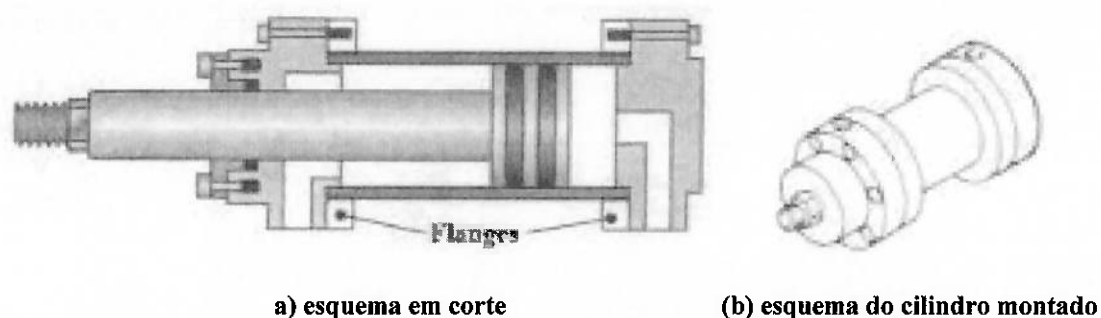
Cilindro diferencial com flanges aparafusadas
